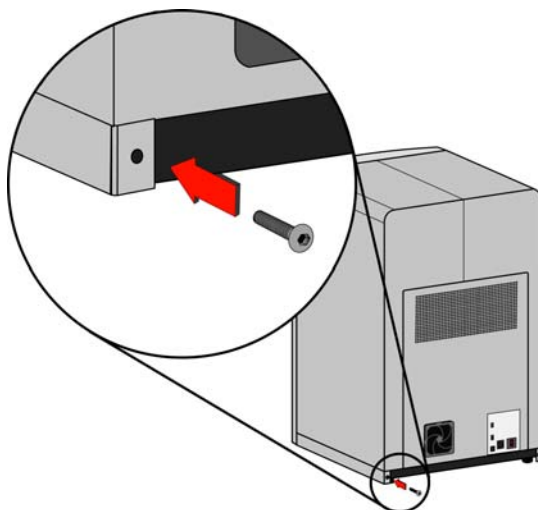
Instalación de las cubiertas de acceso del montacargas de horquilla
